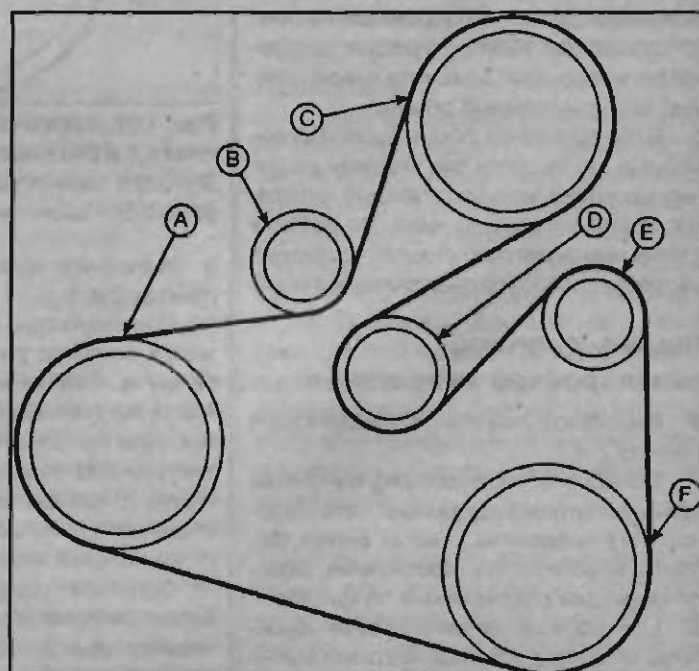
Расположение ремня привода навесных агрегатов на шкивах двигателя 1,8 л с системой кондиционирования воздуха: А – шкив коленчатого вала; В – шкив автоматического механизма натяжения ремня; С – шкив насоса усилителя рулевого управления; D – направляющий шкив; E – шкив генератора; F – шкив компрессора системы кондиционирования воздуха
